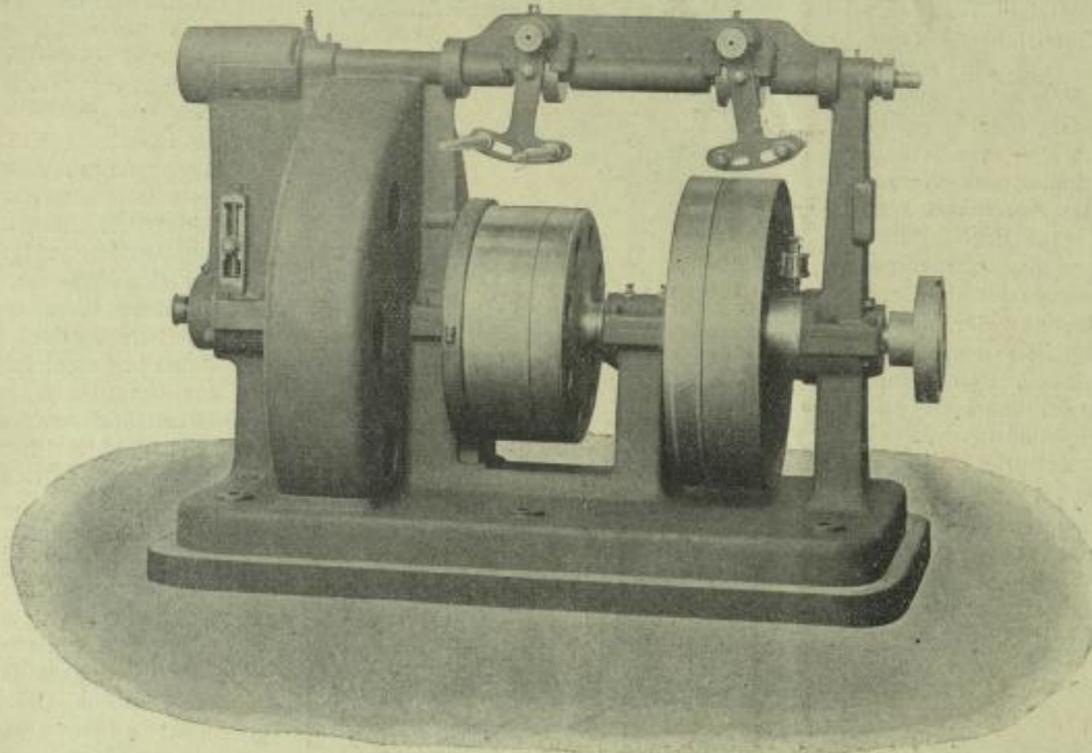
(Zu Hilfsumsteuerung für Werkzeugmaschinen.)
